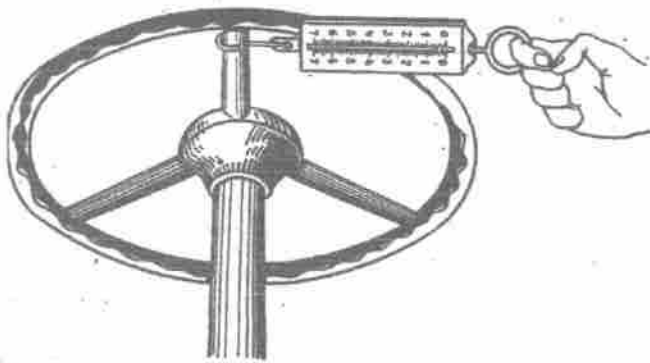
Prüfen des Anzugs der Schneckenlager mit Hilfe eines Dynamometers
